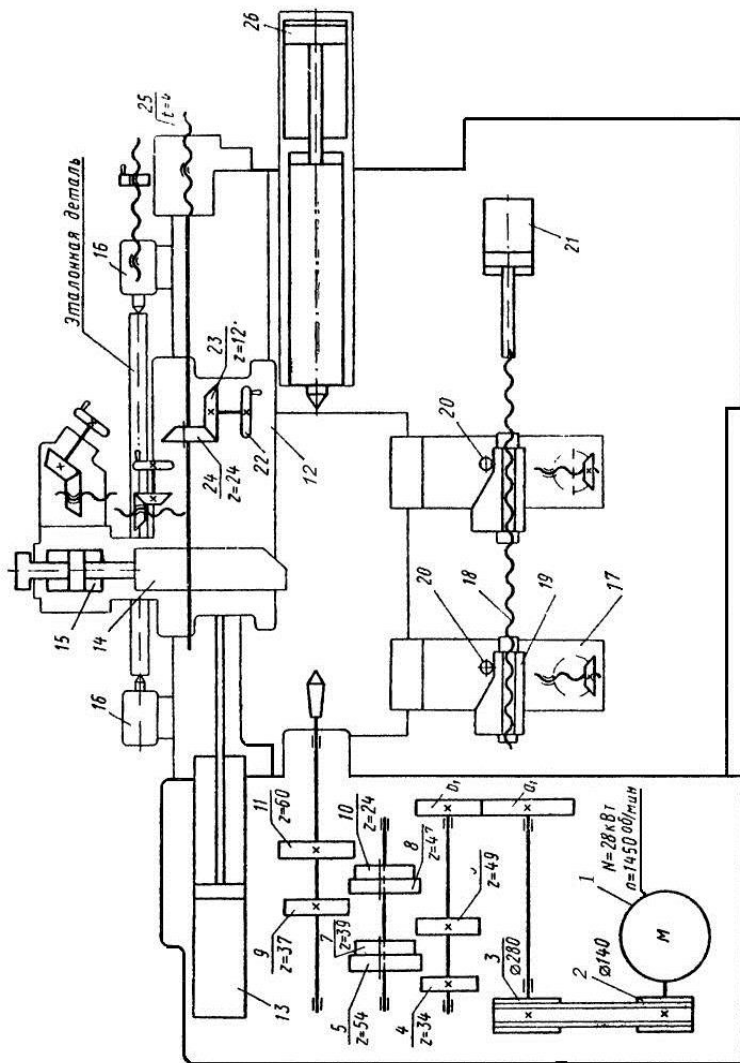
Кинематическая схема станка-полуавтомата мод. 1722
